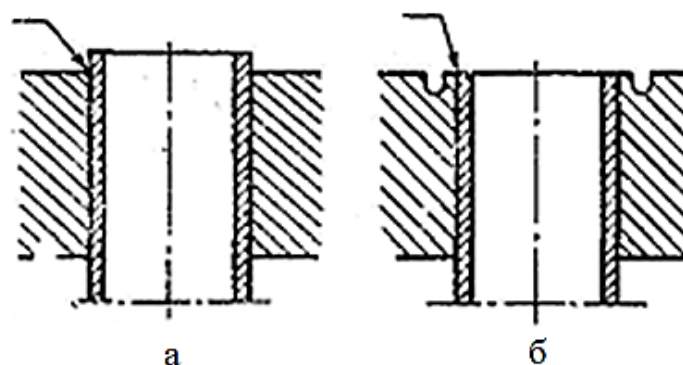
Способи кріплення труб зварюванням: а) кутовим швом;
